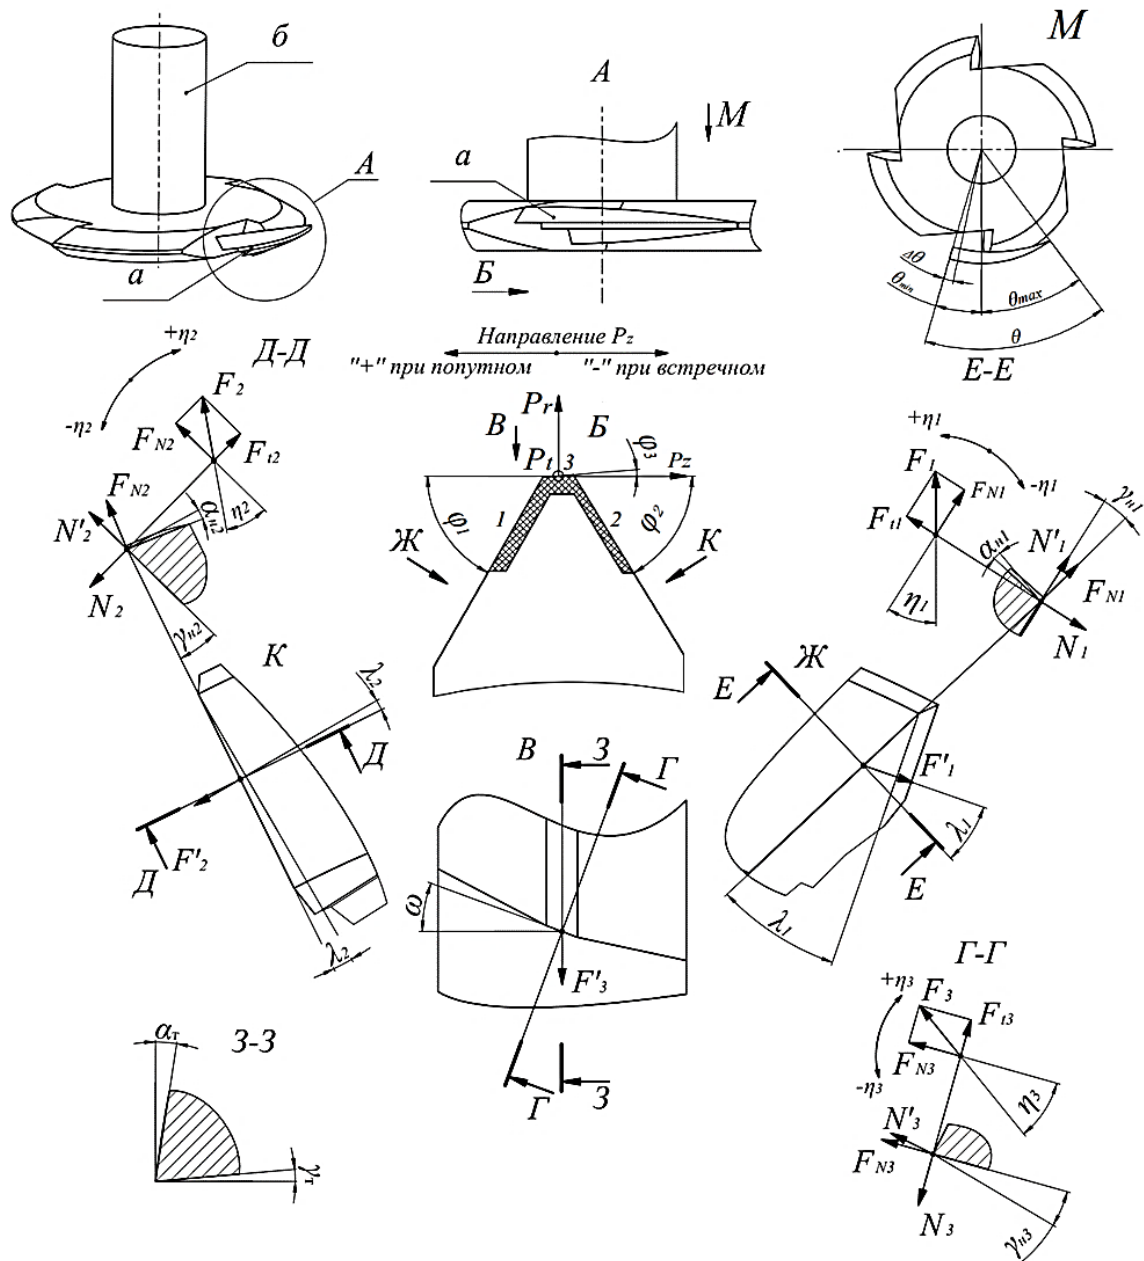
Схема расчета составляющих силы резания на режущей части однодисковой резьбовой фрезы при попутном и встречном направлении обработки: а – срезаемый слой; б – фреза дисковая; 1, 2 – боковые стороны резьбообразующего профиля; 3 – фаска резьбообразующего профиля
